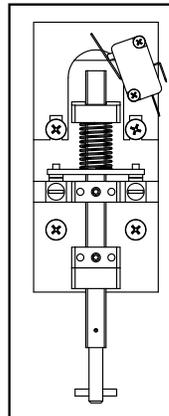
Manuelle Zonenkontaktschalterbaugruppe. Wird für manuelle Installationen oder drahtlose Türsteuerungen verwendet.
